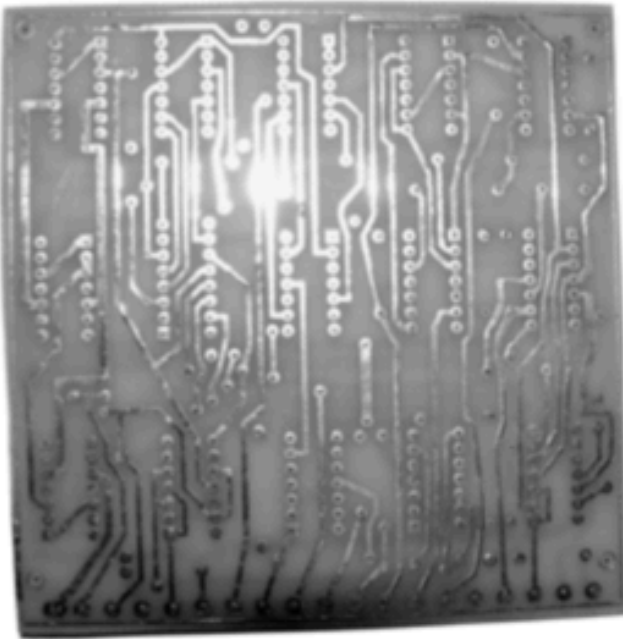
Заготовка платы для ключа с памятью Е. Кургина (UG6AD). Вид со стороны, изготовленной по методу ЛУТ
